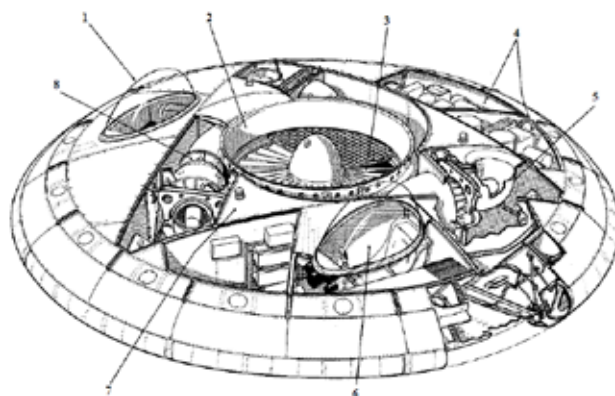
Схематическое изображение VZ-9-AV Avtocar. 1. Кабина наблюдателя. 2. Воздухозаборник 3. Сборка турборотора. 4. Задний грузовой багажник. 5. Вход двигателя. 6. Кабина оператора. 7. Бак топлива. 8. J69-T-9 реактивный двигатель
